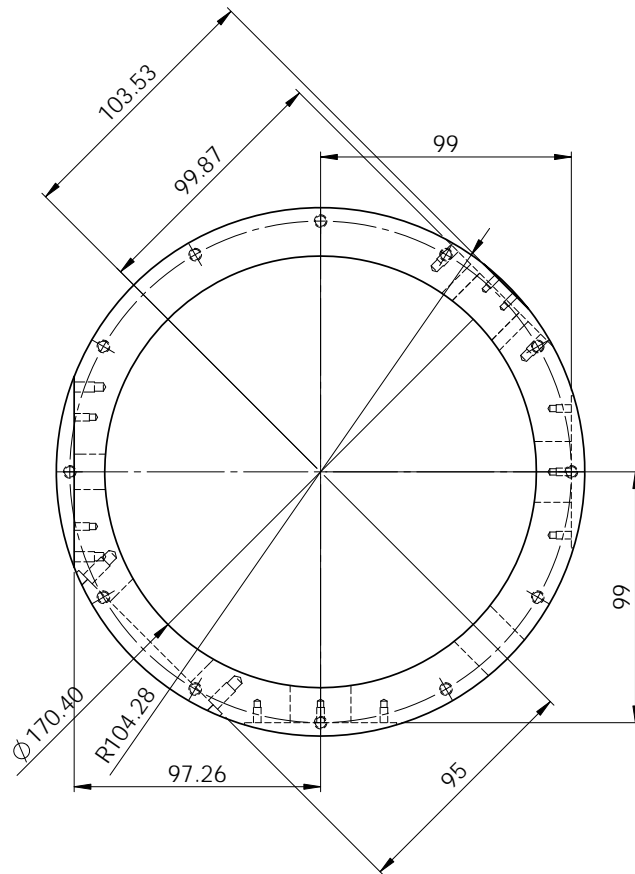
Technische Zeichnung der Vakuumröhre, Ansicht von oben.
